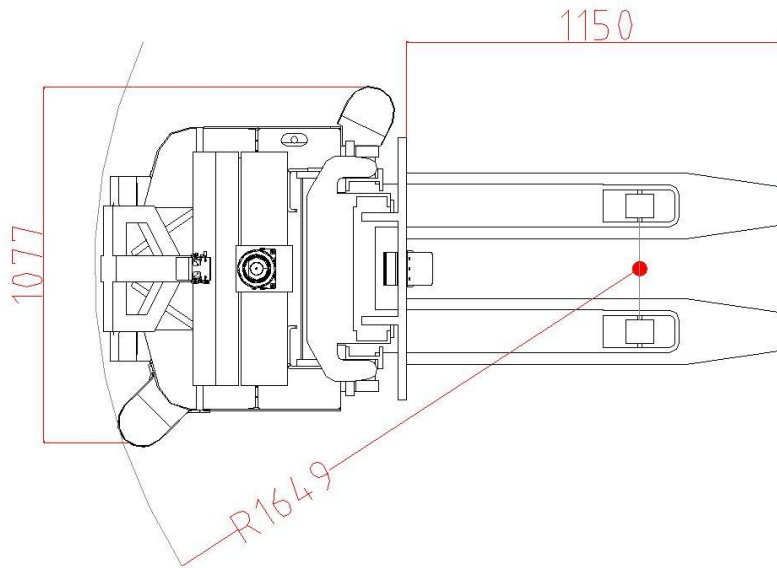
Vista en planta del AGV EGV-S20
